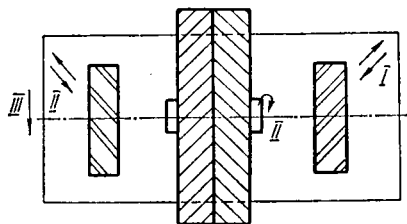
Схема и направление основных движений при нарезании прямозубых колес зубчатыми гребенками
